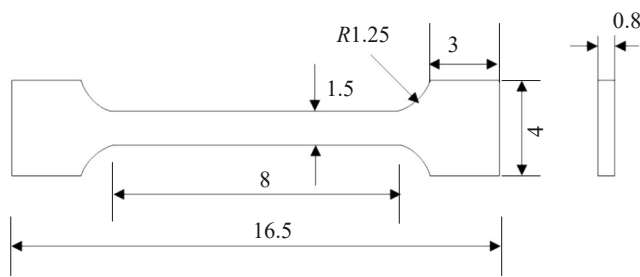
LPBF成形 Inconel 738合金的室温拉伸尺寸
